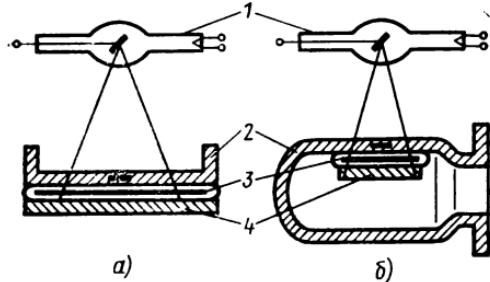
Контроль плоской отливки (а) и отливки для работы под давлением (б) рентгеновскими лучами:
